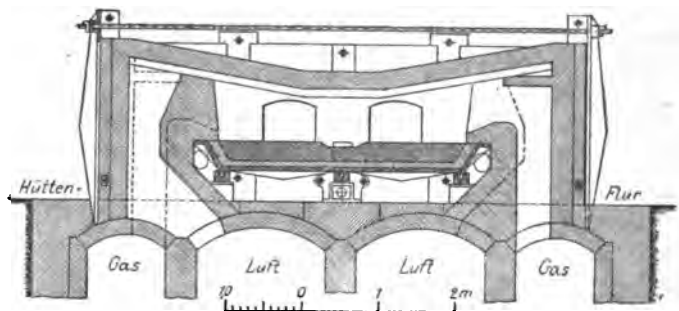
Schweißofen mit Umschaltfeuerung aus dem Beginn der Achtziger Jahre.
